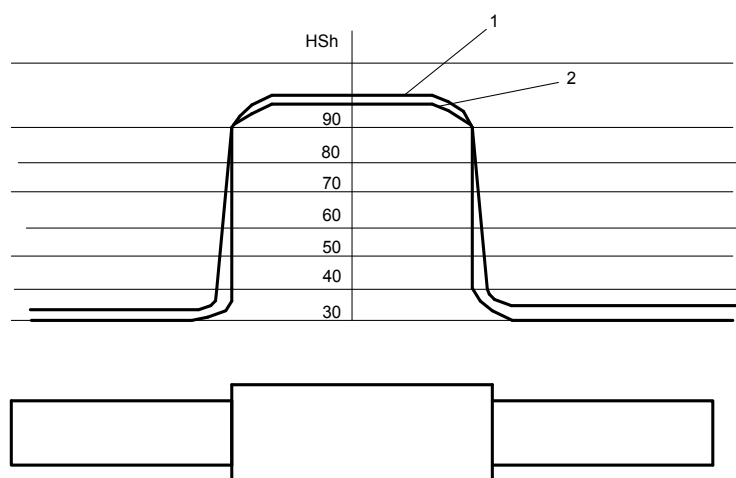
7 – Общий вид наплавленного рабочего валка после механической обработки
